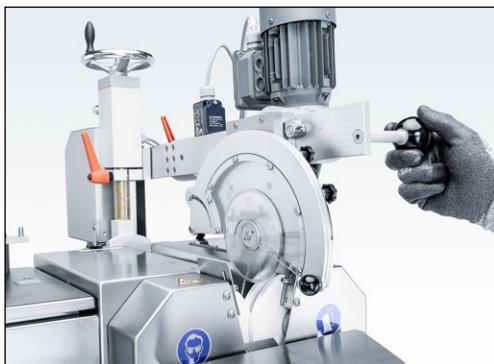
Установка приспособления для заточки дисковых ножей в положение заточки
